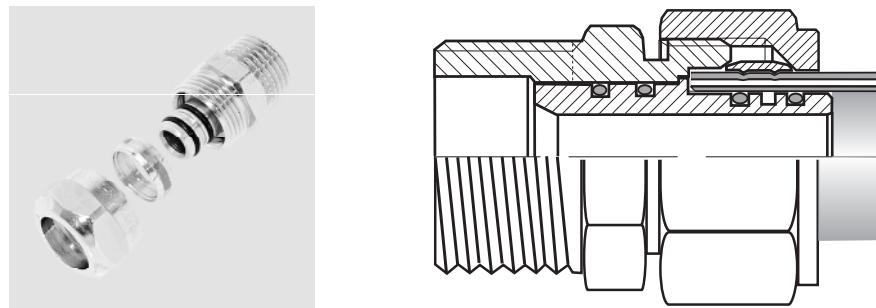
Разрезы соединителей VESTOL и VESTOL ZBK
